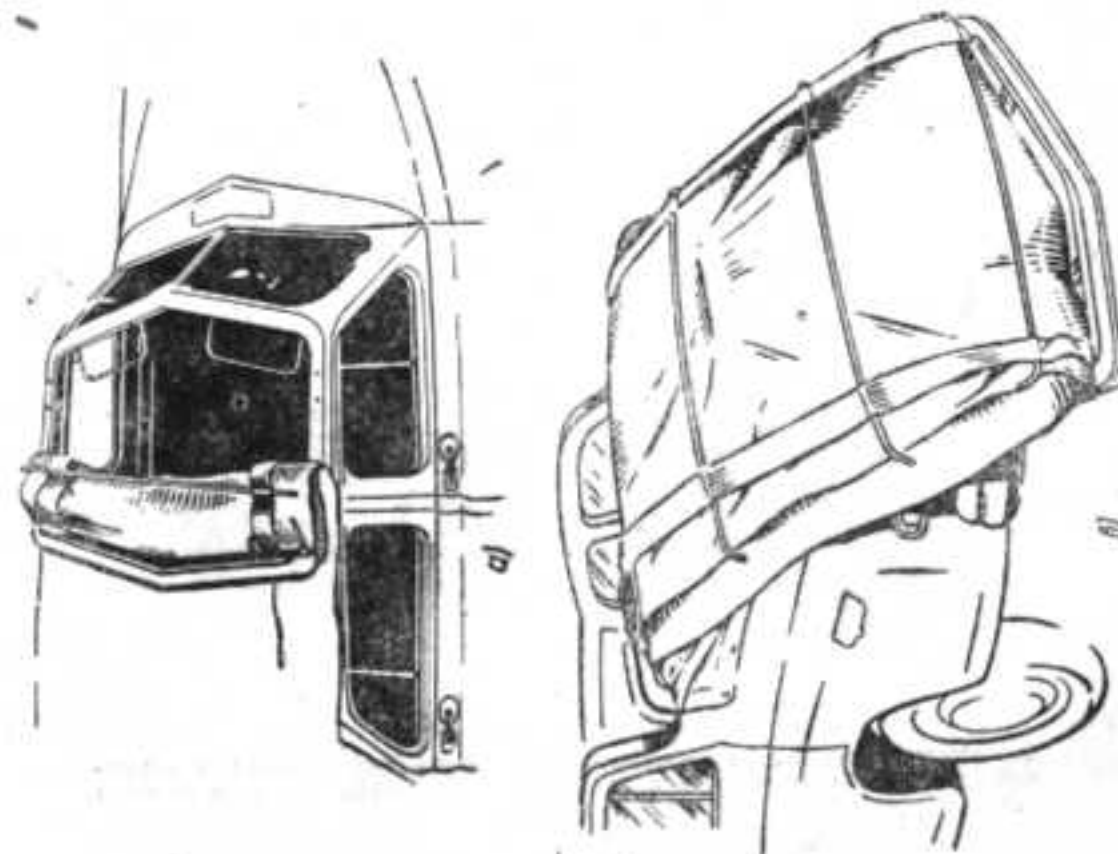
Вынимание воздушного фильтра системы отопления через люк вентиляции:
